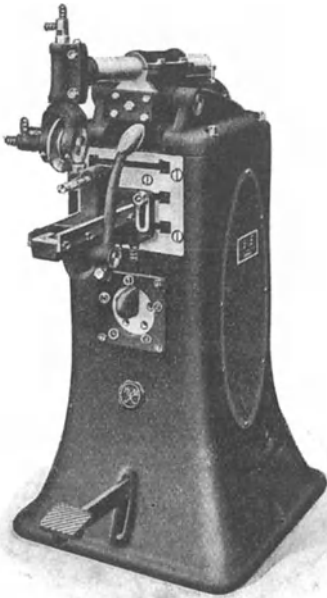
Längsnahtmaschine für Blechzylinderschweißung.
